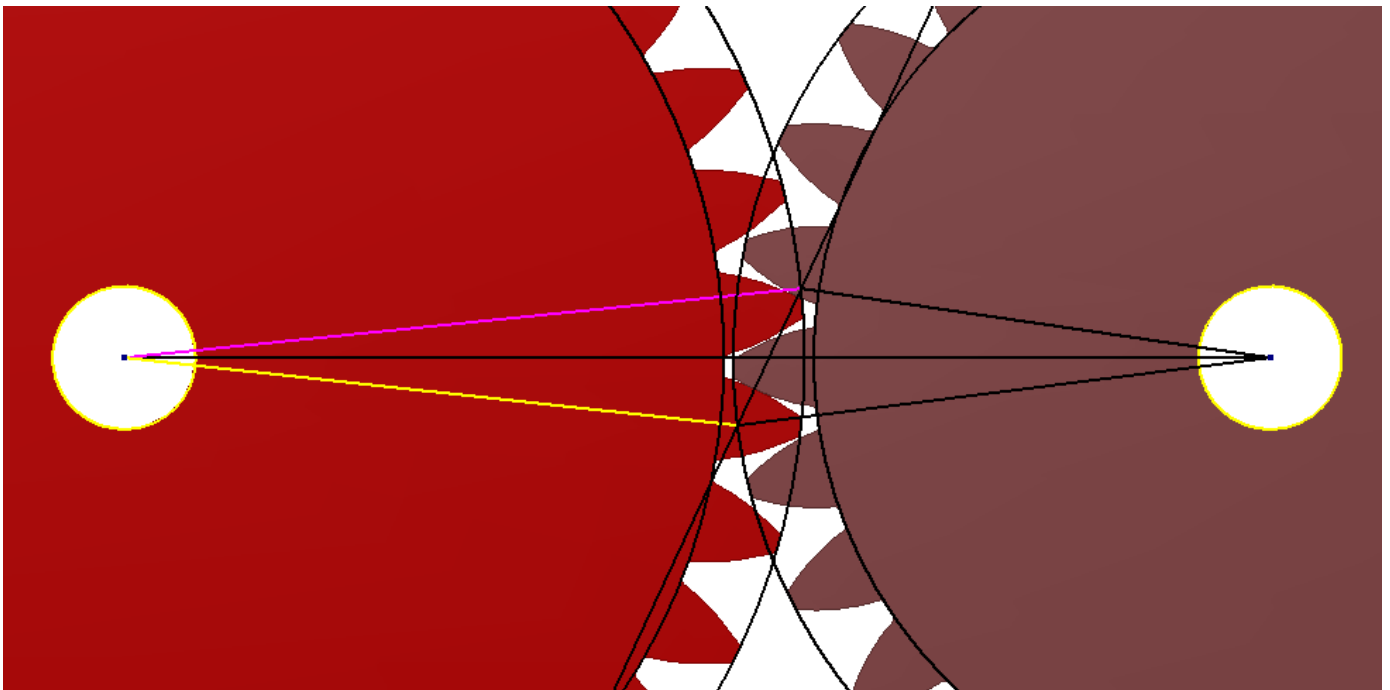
Punto inicial y final de contacto de dos dientes.
